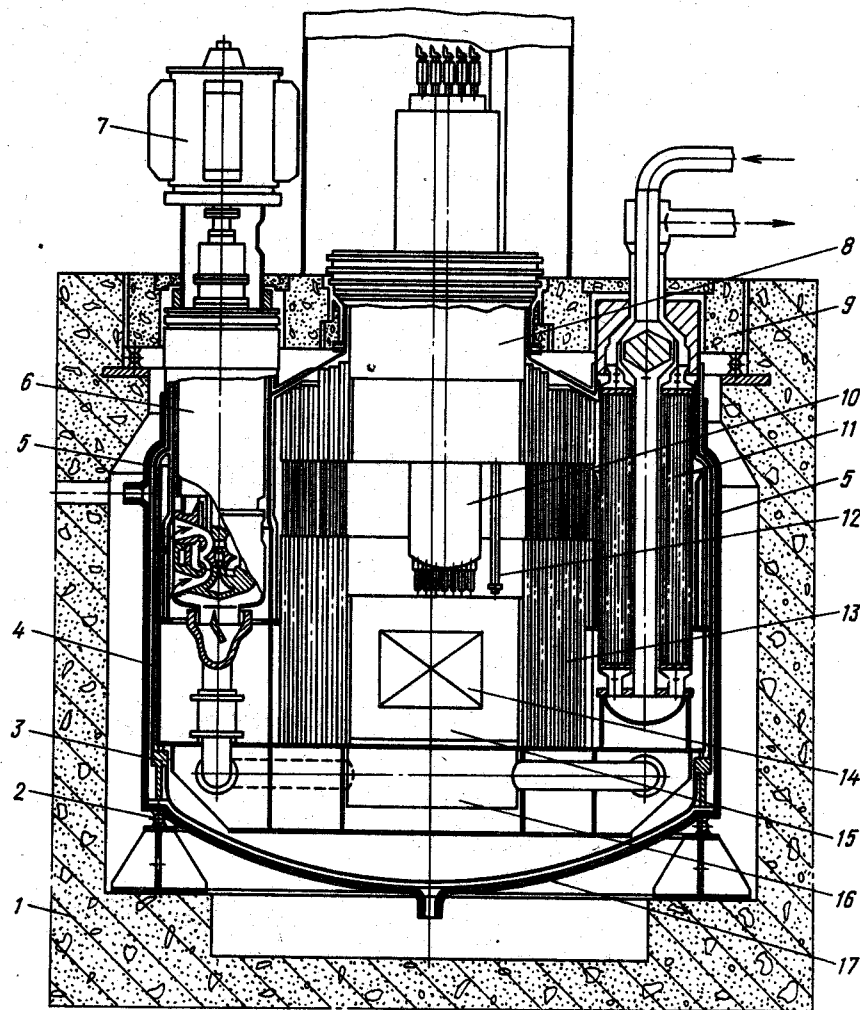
Вертикальный разрез реакторной установки БН-600:
